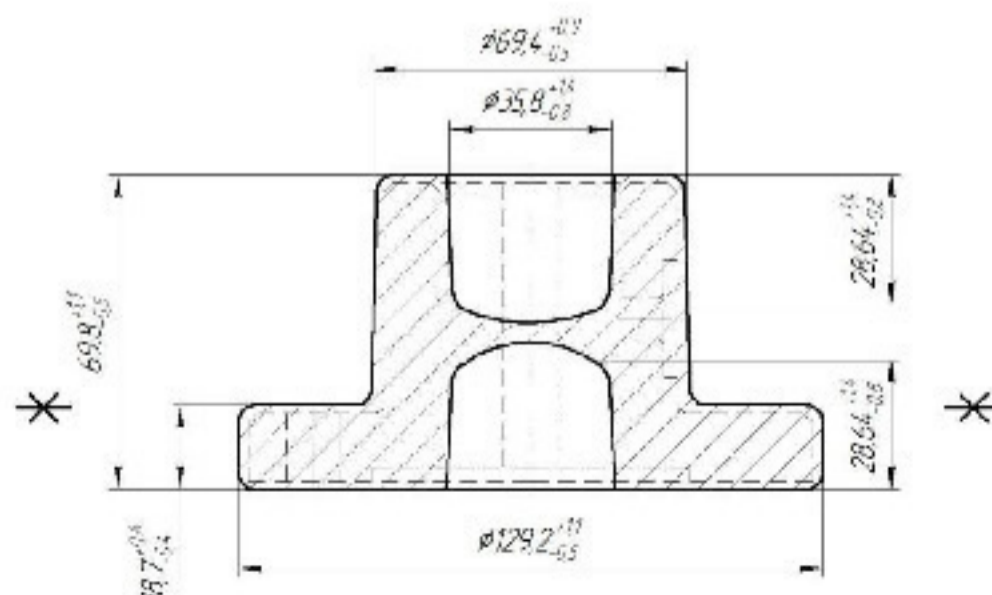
Ескіз заготовки при штампуванні на КГШП
